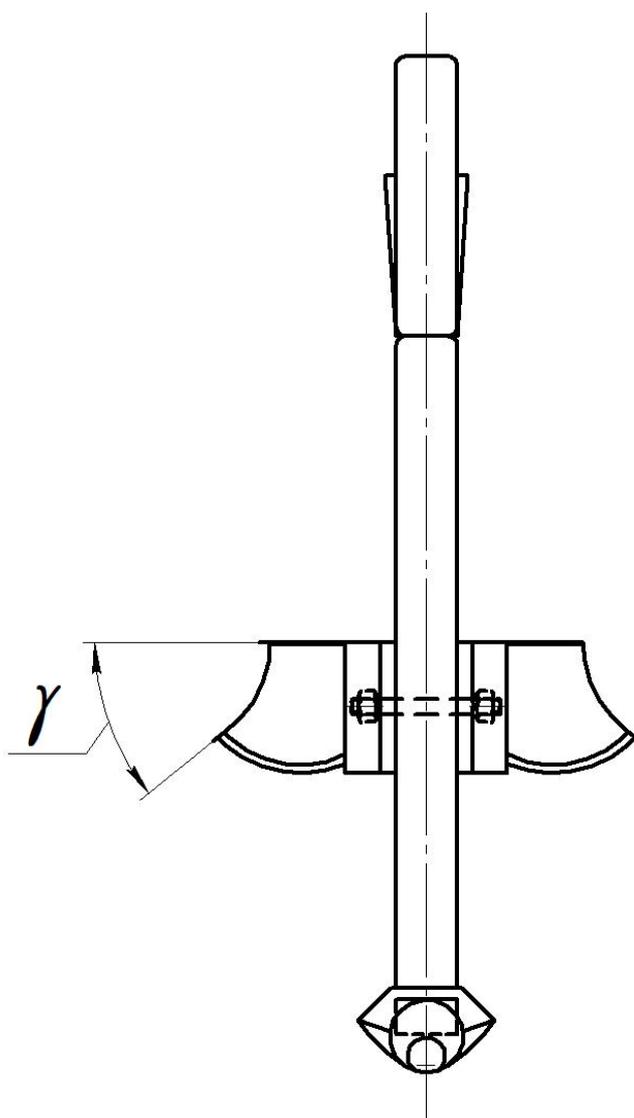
Новый рабочий орган глубокорыхлителя для технологии «strip-till» (вид А):
